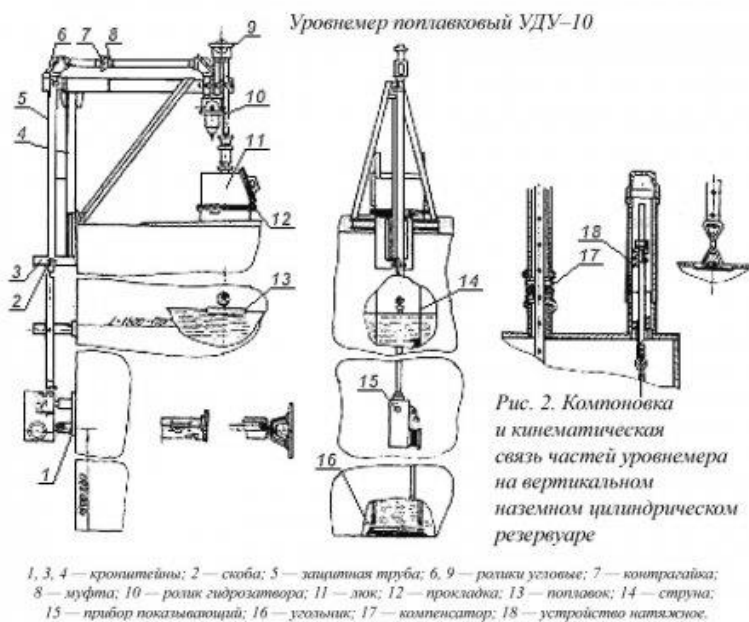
Компоновка и кинематическая связь частей уровнемера на вертикальном наземном цилиндрическом резервуаре
